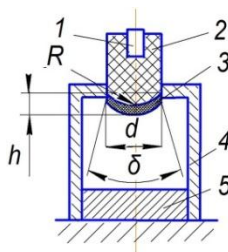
Принципиальная схема установки, обеспечивающей СГП частиц с максимальным охватом площади обработки, 1 – детонатор, 2 – заряд ВВ, 3 – метаемый порошок, 4 – корпус, 5 - заготовка
